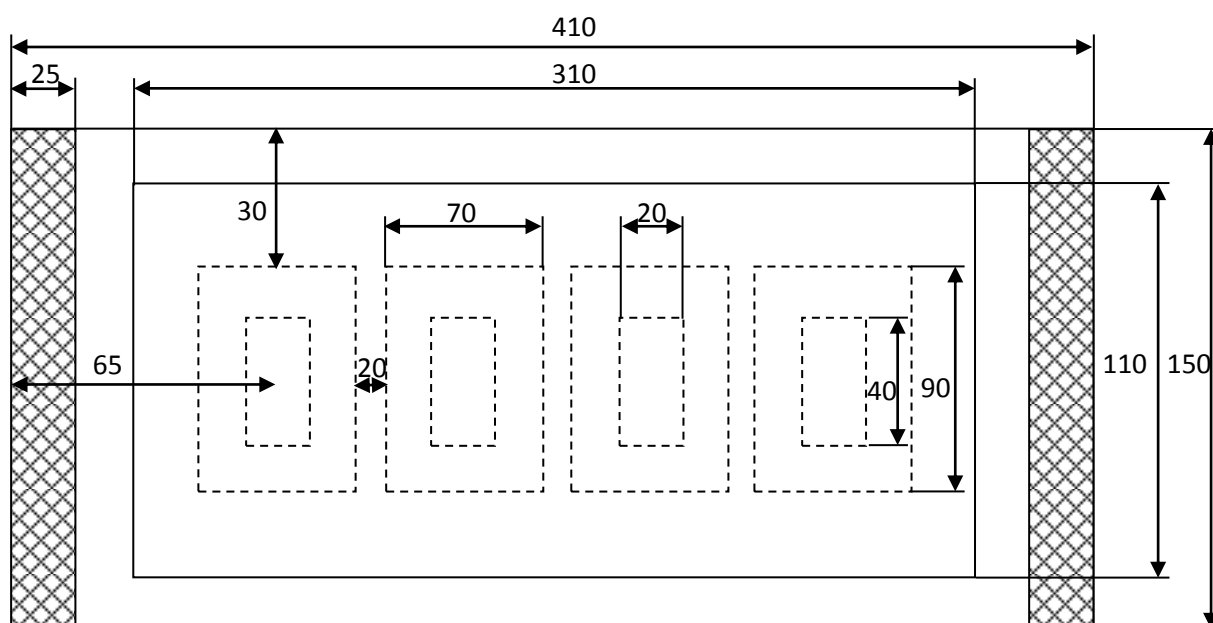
Эскизный рисунок опытного образца ТЭС с основными геометрическими размерами
